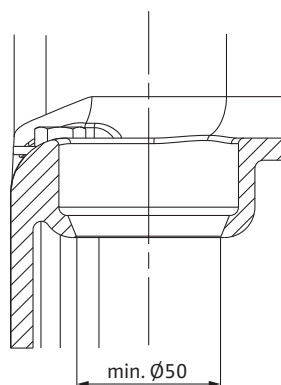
Aansluiting aanzuigleiding voor handmembraanpomp
